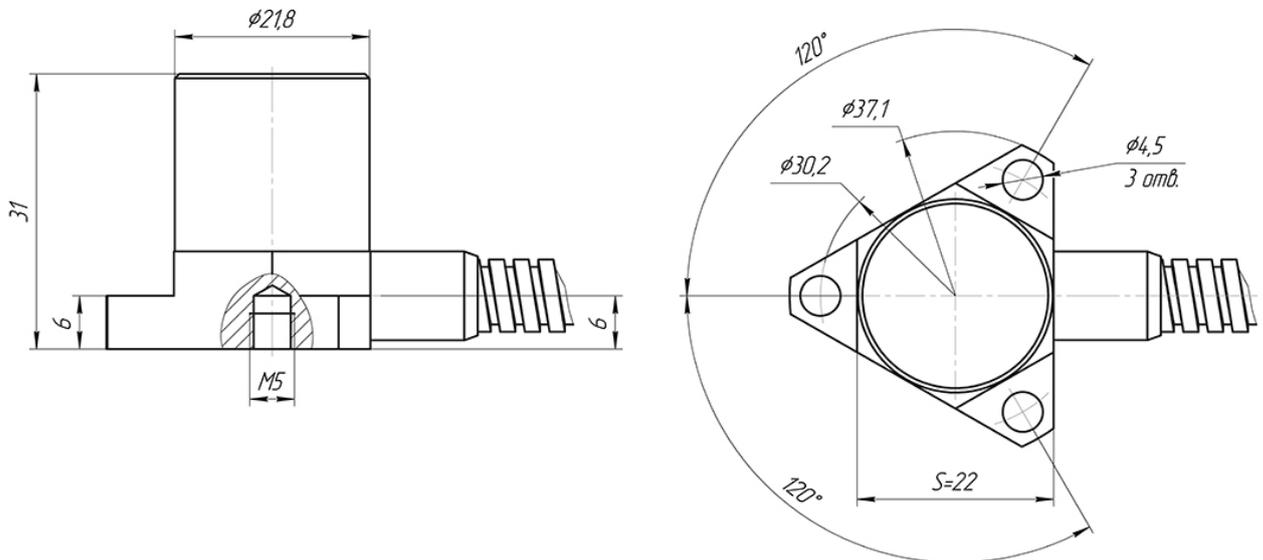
Габаритный чертеж акселерометра ZET 112
